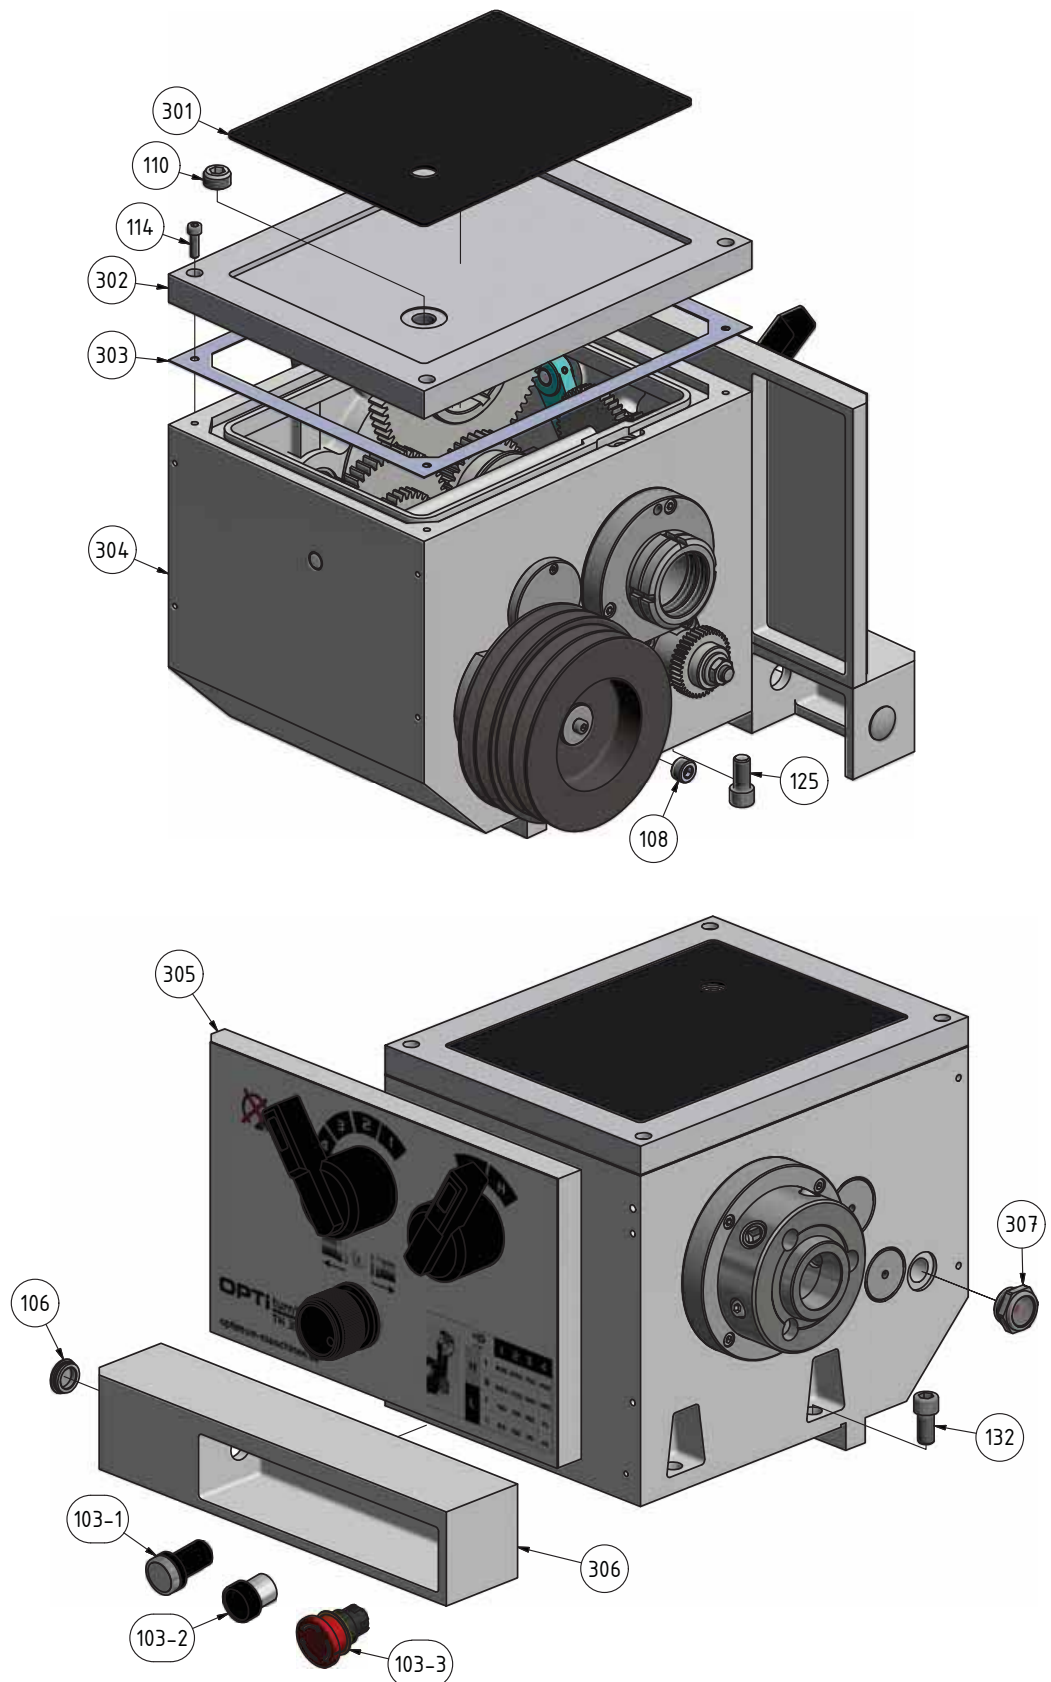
Getriebe Spindelstock 1-6 - Headstock gear 1-6
